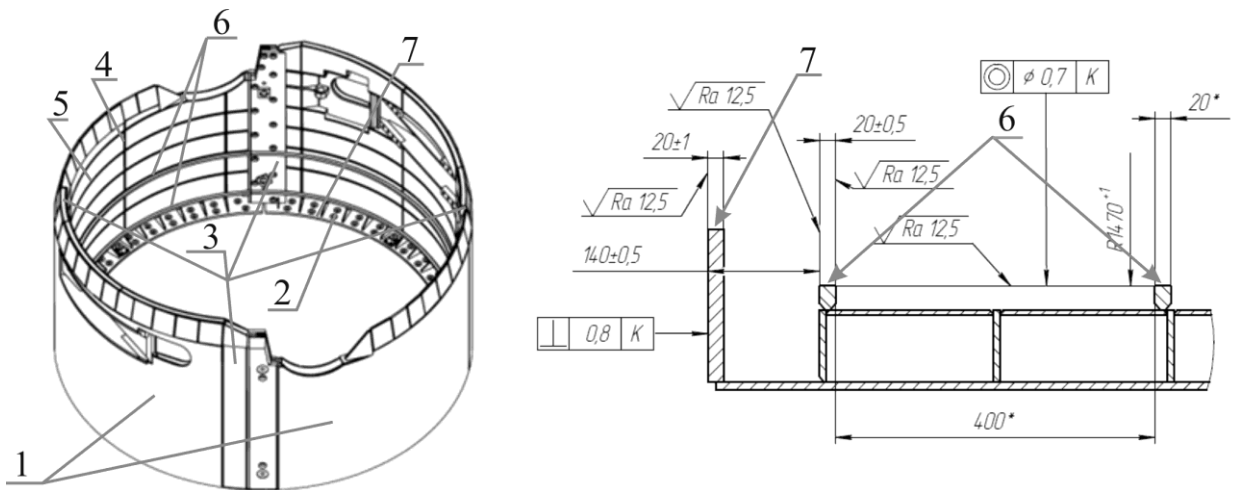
Общий вид головной секции геохода (1 – обечайки; 2 – фланцы; 3 – замки; 4 – стрингеры; 5 – шпангоуты; 6 – дорожки качения; 7 – внутренняя поверхность соединительного фланца).
